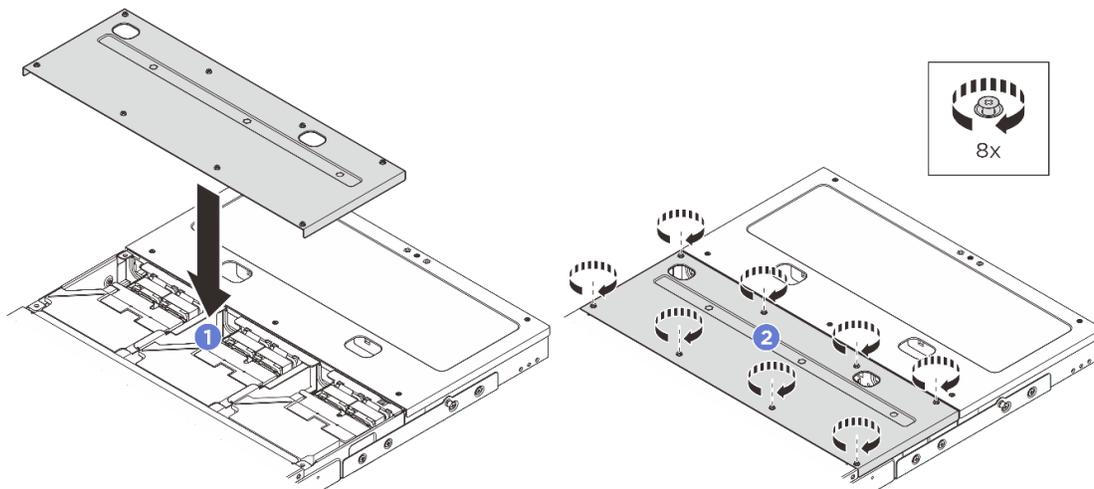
Установка среднего верхнего кожуха корпуса 1U3N
